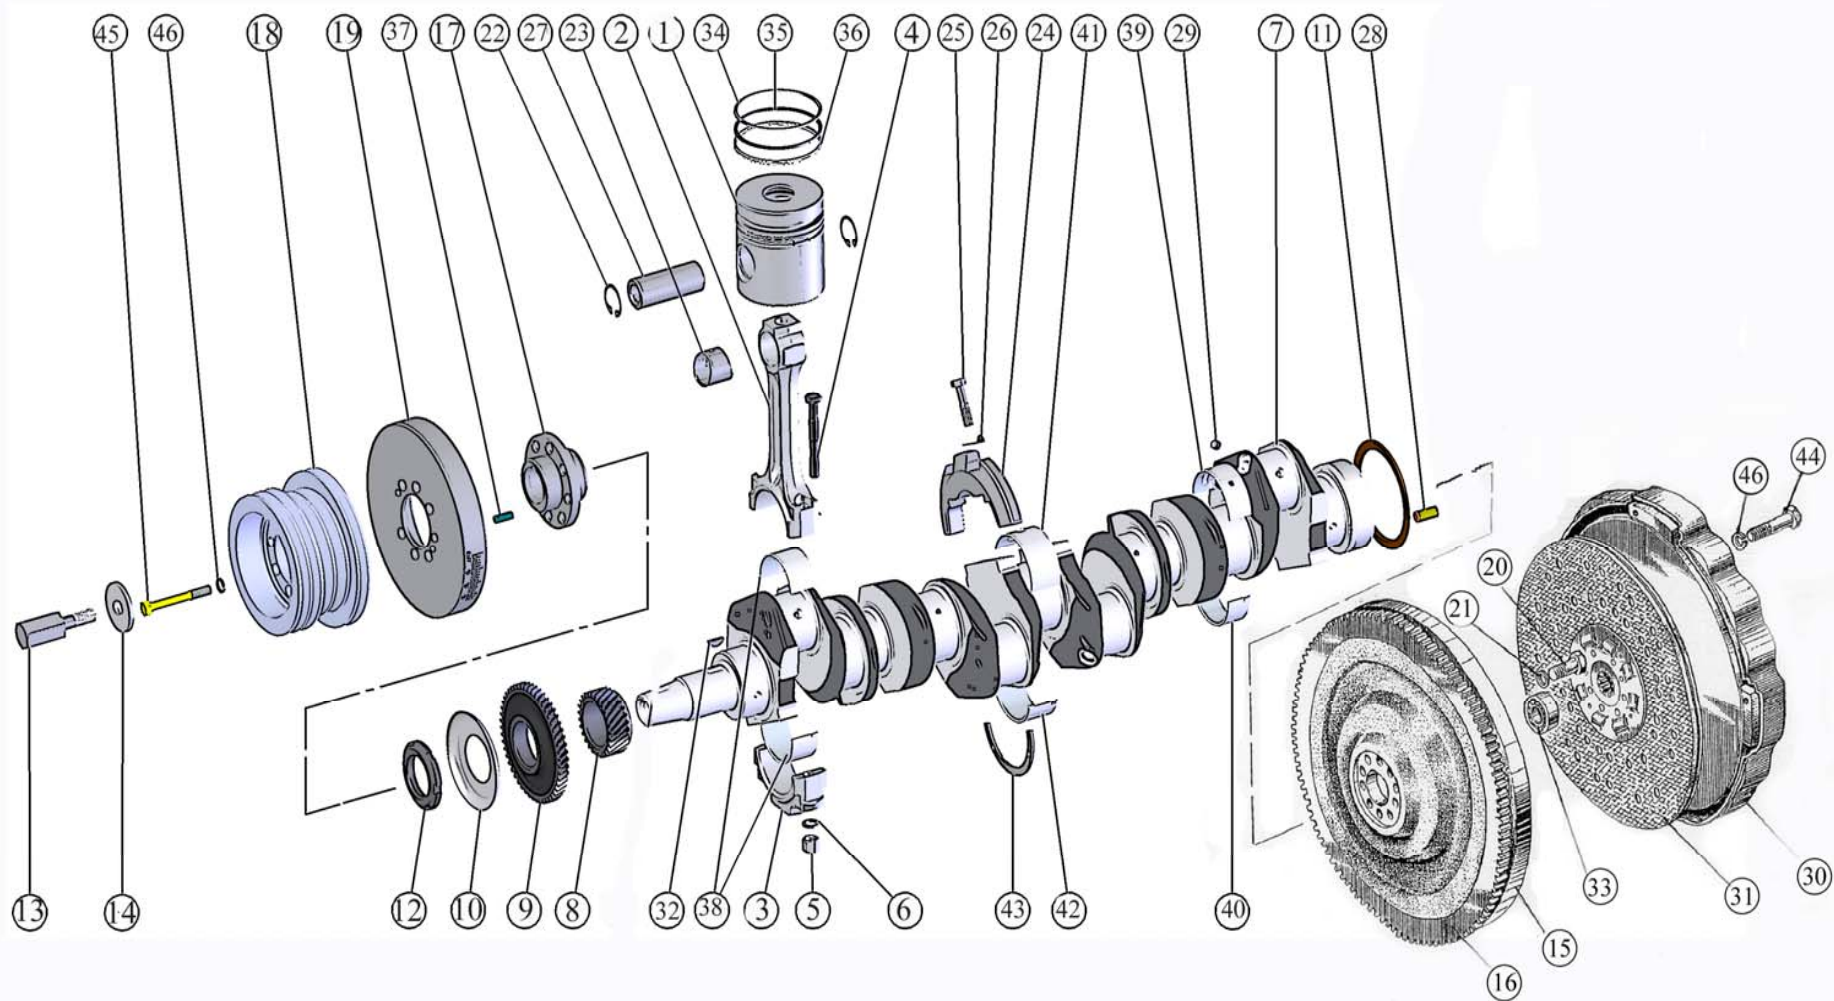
Поршни и шатуны. Коленчатый вал и маховик
